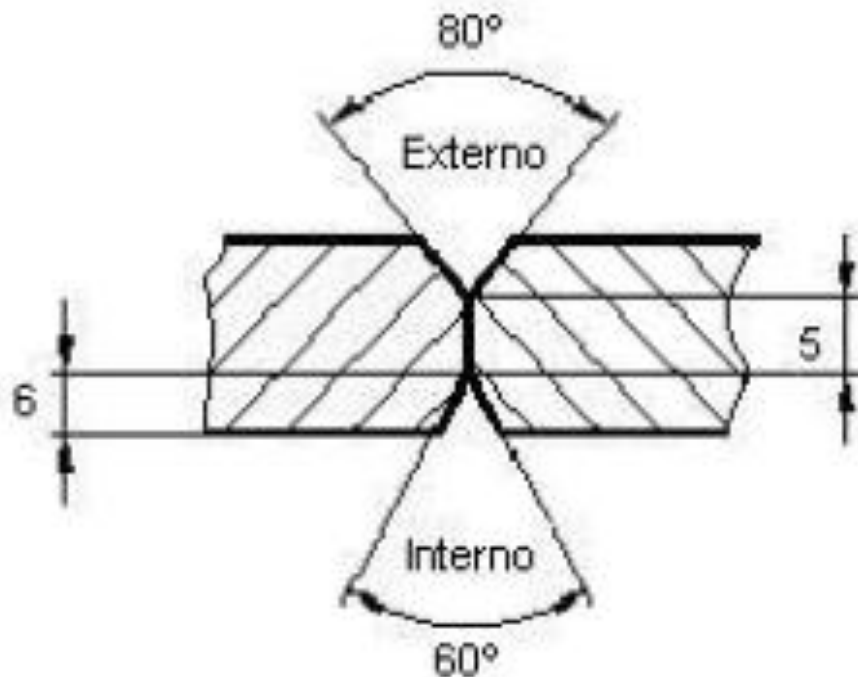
Detalhe do chanfro da chapa a ser soldada.
